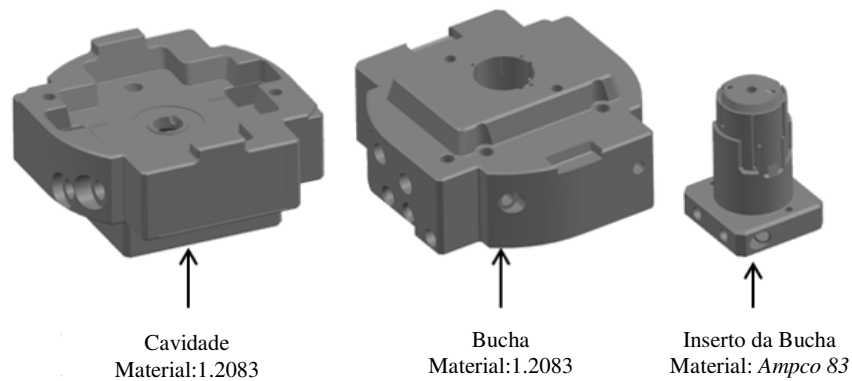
Zonas moldantes do molde de fabrico convencional, *Sensor housing
